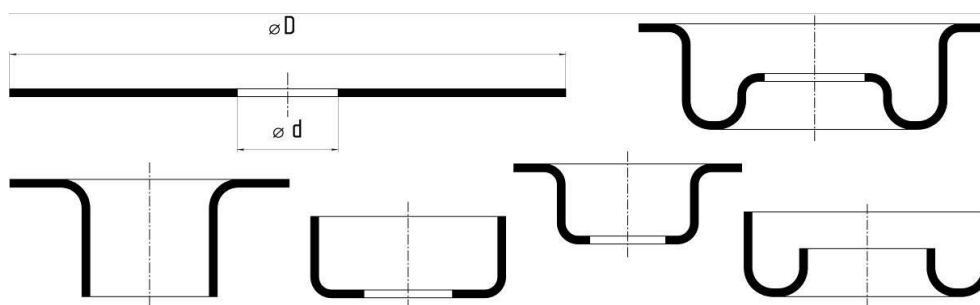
Плоская кольцевая заготовка и полуфабрикаты, полученные из нее формообразующими операциями листовой штамповки
